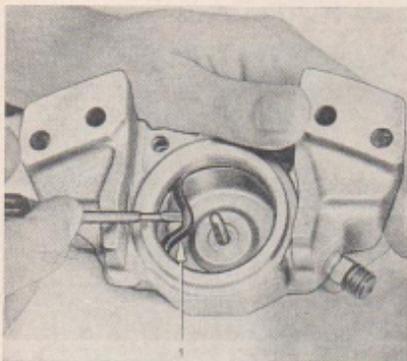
Gummdichtung für Kolben aus Nut im Zylinder des Sattelgehäuses herauswälzen
